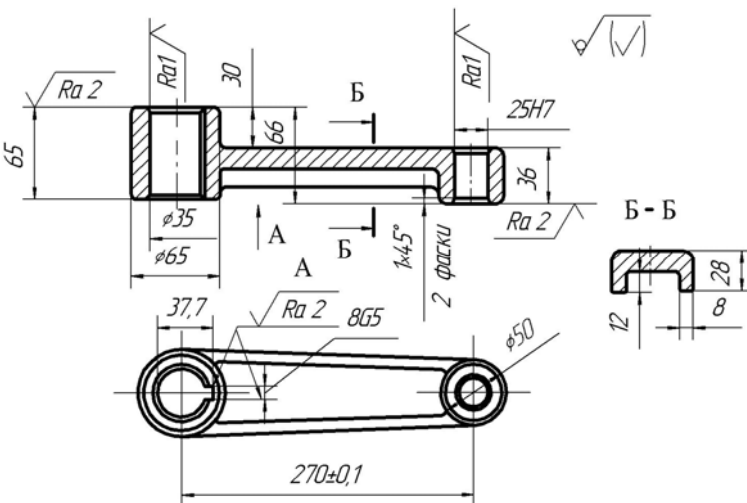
Приклад кресленика деталі, форму якої виявляють за допомогою розрізу, виду й перерізу
